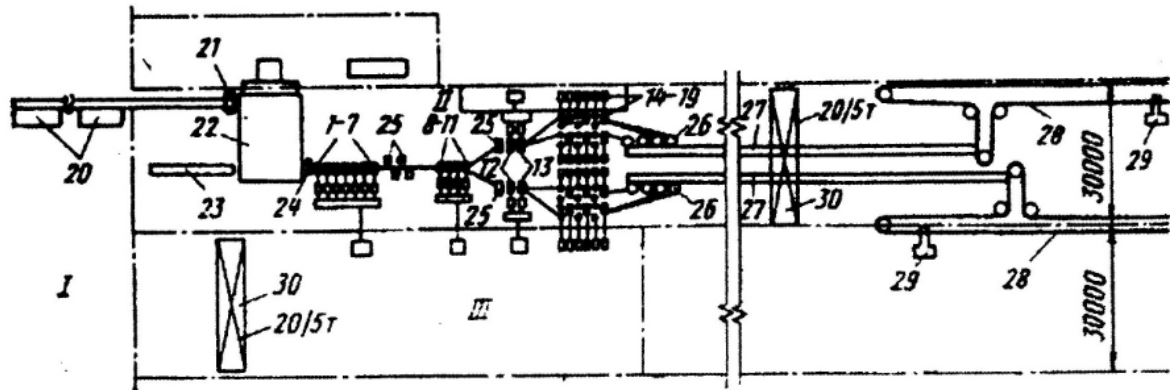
Схема розташування обладнання безперервного дротового стану 250 для паралельної прокатки чотирьох ниток дроту: I – склад заготовок; II – становий проліт; III - машинний зал; 1...7 – чорнові кліті першої групи; 8...11 – чорнові кліті другої групи; 12, 13 – перед чистові кліті; 14... 19 – чистові кліті; 20 – завантажувальна решітка; 21 – заштовхувач; 22 – нагрівальна піч; 23 – виштовхувач; 24, 25 – ножиці; 26 – моталки; 27 – транспортери; 28 – гаків конвеєр; 29 – пакувальний устрій; 30 – кран.
